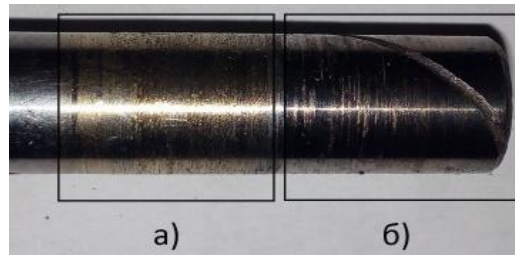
Контртело после испытаний на трение: а – образец № 2; б – образец № 1
